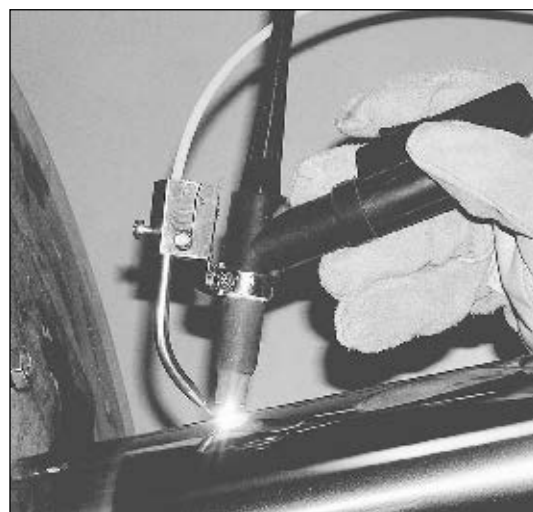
Ручная ТИГ сварка с механизированной подачей присадочной проволоки
